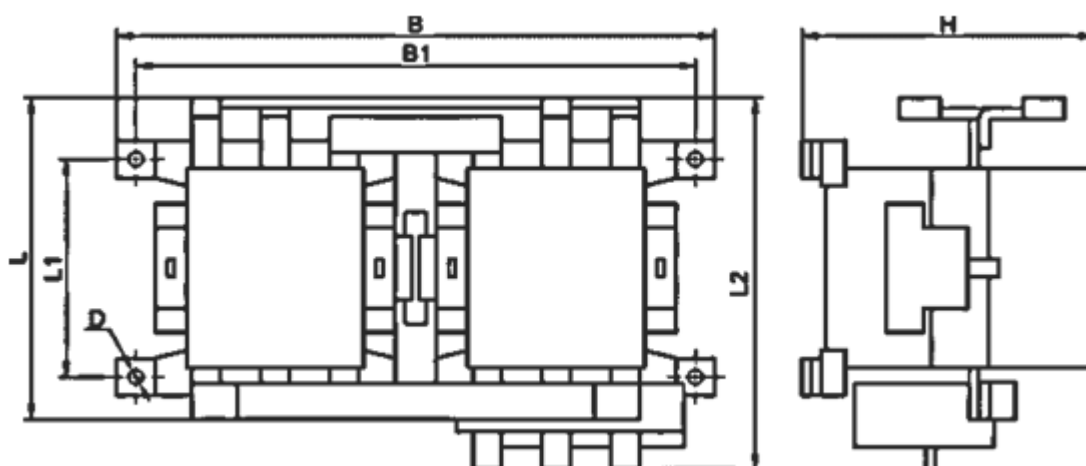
Пускатель реверсивный ПМ12 100-250А
